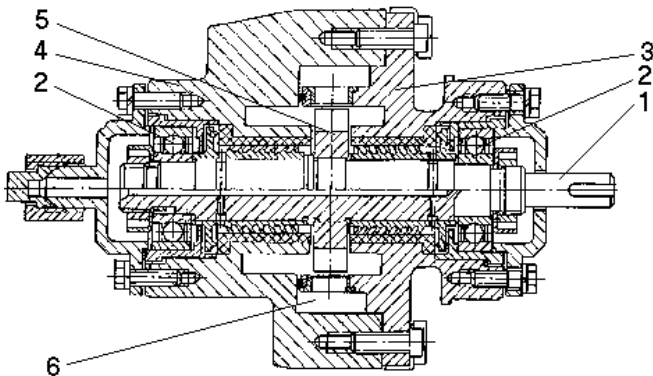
Конструктивная схема генератора колебаний давления (пульсатора): 1- приводной вал; 2- подшипник; 3- крышка корпуса; 4- корпус; 5- модулирующий диск; 6- объем, связанный с рабочей камерой генератора
